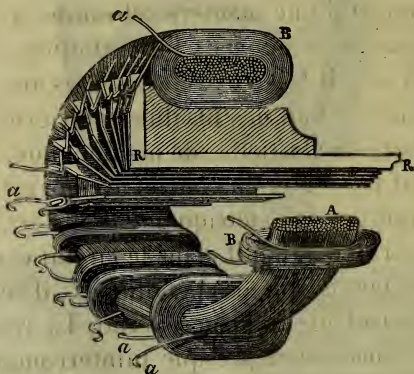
Anneau de la machine Gramme. (*La Lumière électrique.*)
